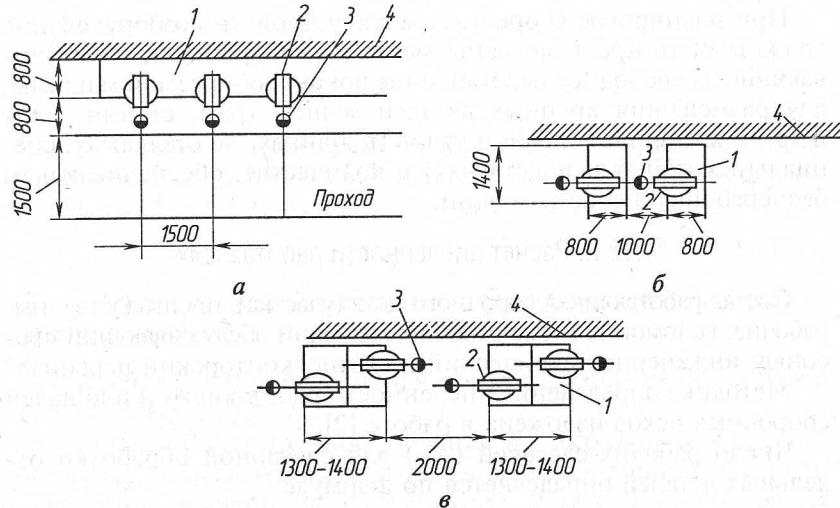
Схема расположения слесарных верстаков: а — продольное; б — поперечное; в — поперечное двухсторонних верстаков; 1 — верстак; 2 — тиски; 3 — рабочее место; 4 — стена
